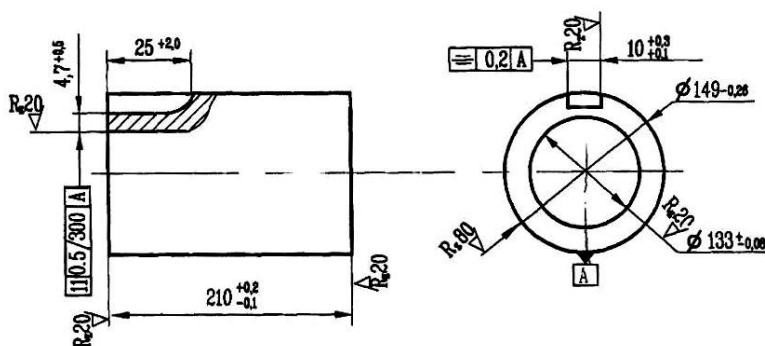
Чертеж заготовки корпуса стартера после выполнения операции фрезерования
